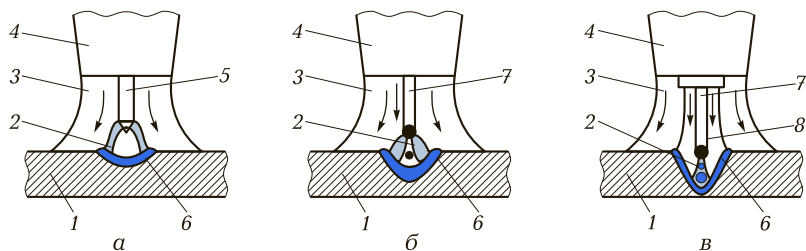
Схемы процессов сварки в защитных газах:
